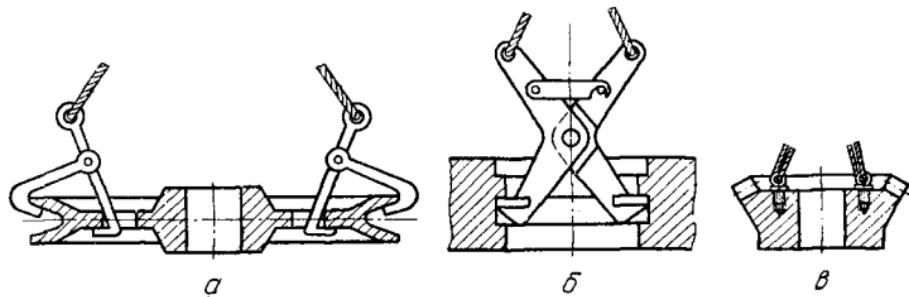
Схемы строповок деталей типа шкивов, шестерен и т. п. для установки их на станки:
